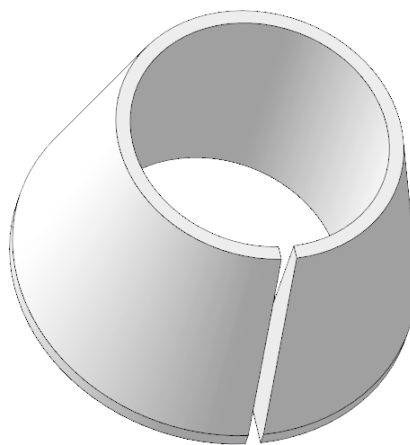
Елемент рухомого з'єднання, виготовлений із самозмащувального композитного матеріалу
